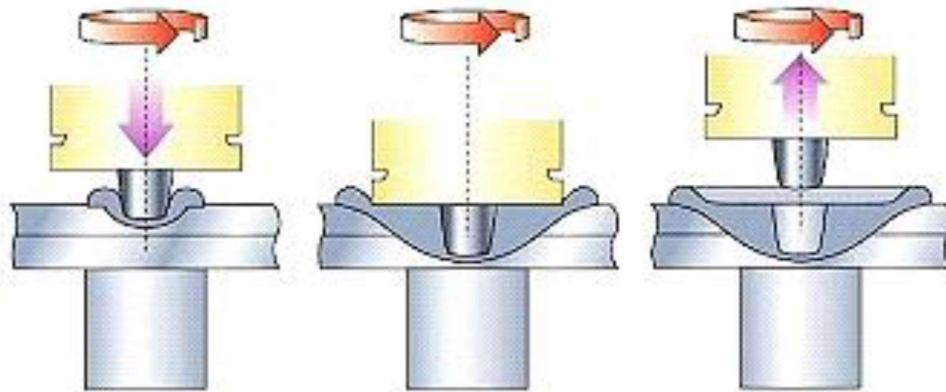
Étapes du procédé de soudage FSW par point. [5]
